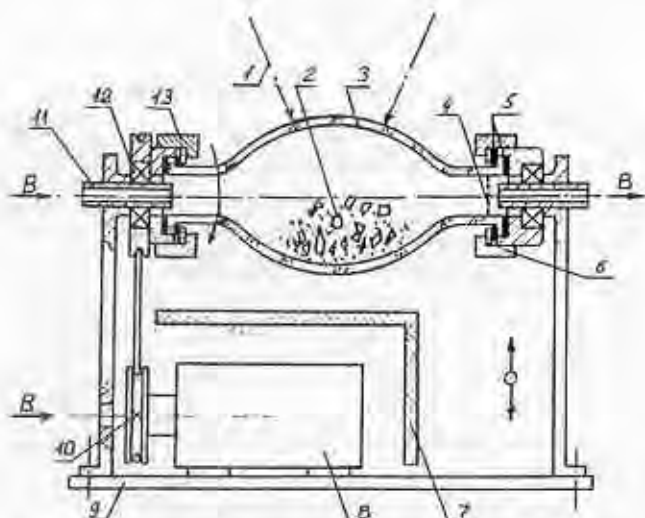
Схема устройства для термической обработки порошков и мелких изделий в солнечных и оптических печах: 1 — лучистый тепловой поток; 2 — нагреваемый объект; 3 — кварцевый реактор; 4 — металлическая сетка; 5 — прокладка; 6, 13 — прижимные гайки; 7 — теплоизолирующий экран; 8 — электродвигатель; 9 — плоская основа; 10 — ведущий шкив; 11 — пустотелый вал; 12 — подшипник; B — сжатый воздух.
